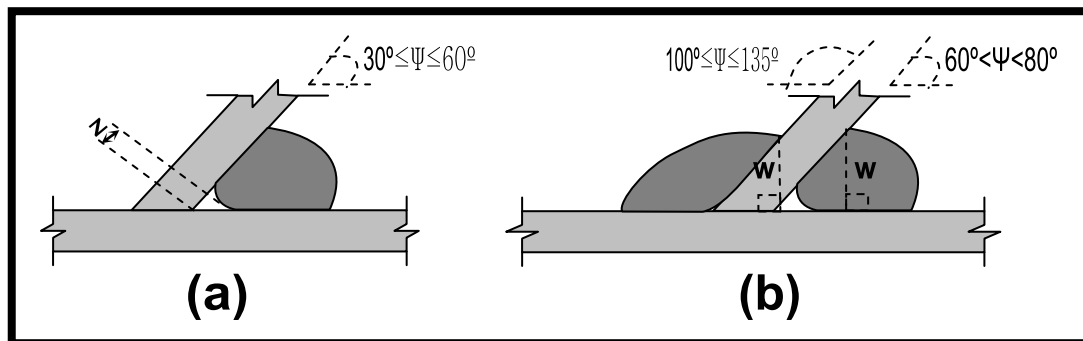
Área efectiva sobre una soldadura de filete para uniones T oblicuas.
